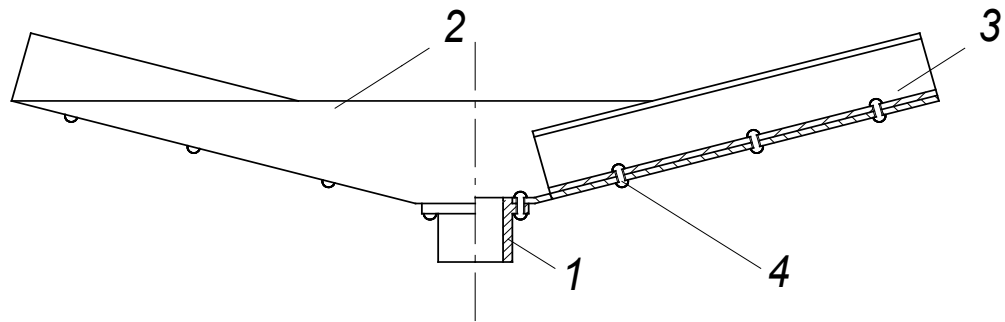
Схема відцентрового РО з диском конічної форми:
